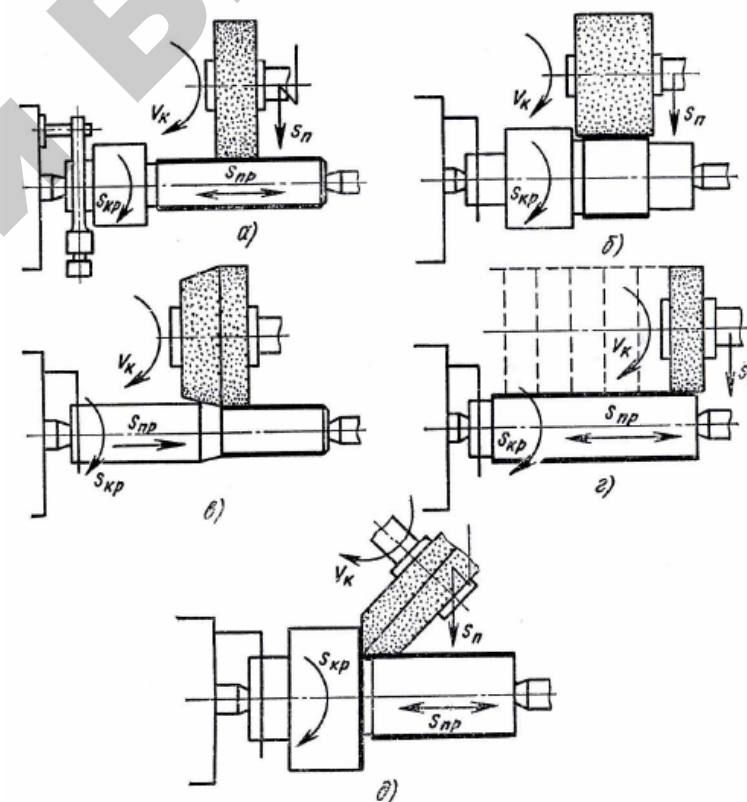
Схемы обработки заготовок на круглошлифовальных станках:
